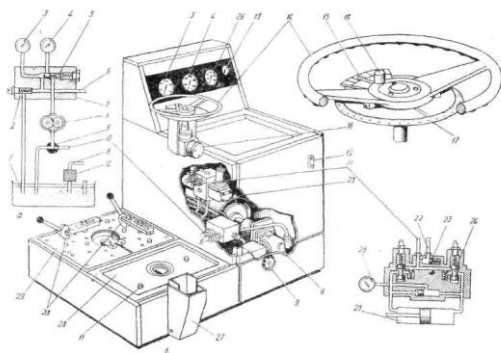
Стенд КИ-4896М для випробування гідропідсилювачів рульового керування: а – схема гідравлічної системи приводу; б – навантажувальний пристрій сошки гідропідсилювача; 1 – витратний гідробак; 2 – запобіжний клапан; 3 – манометр високого тиску; 4 – манометр низького тиску; 5 – клапан відключення манометру низького тиску; 6 – штуцер подачі робочої рідини від насоса до гідро підсилювача; 7 – гідроблок; 8 – насос НШ 10-Е; 9 – кран переключення; 10 – штуцер гідролінії всмоктування насоса; 11 – штуцер зливу робочої рідини у бак; 12 – фільтр; 13 – дистанційний термометр; 14 – рульове колесо; 15 – шкала зусиль динамічного пристрою; 16 – фіксатор; 17 – шкала люфтоміру; 18 – редуктор рульової колонки; 19 – кнопка пускача; 20 – електродвигун; 21 – штуцер підводу до навантажувального пристрою; 22 – зливний штуцер навантажувального пристрою; 23 – редукційний клапан; 24 – напірний золотник; 25 – гідроциліндр навантажувального пристрою; 26 – манометр навантажувального пристрою; 27 – стійка; 28 – ванна; 29 – установочна плита; 30 – затискачі.
